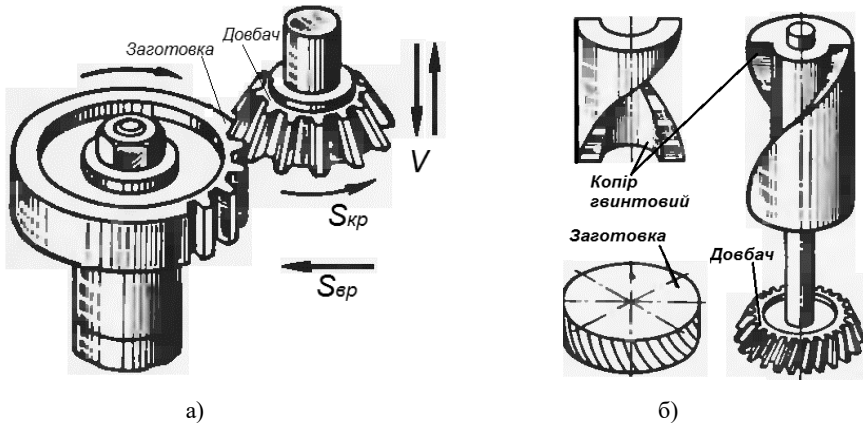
Схеми нарізування зубчастих коліс довбанням: а – прямозубих; б – косозубих
